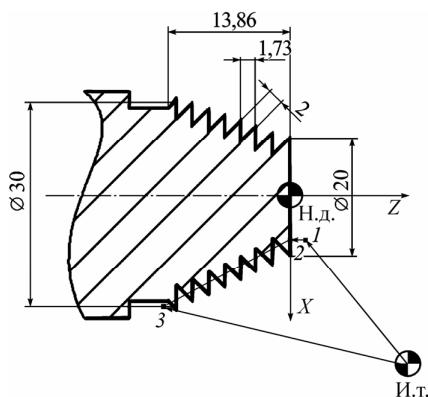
Пример нарезания цилиндрической резьбы с увеличивающимся шагом
